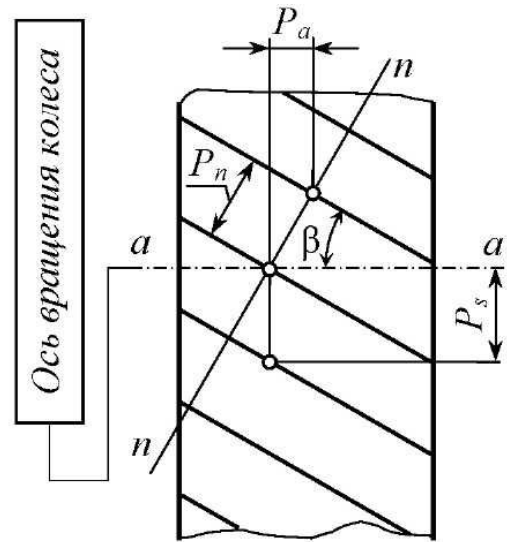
Схема расположения зубьев на косозубой зубчатой рейке
